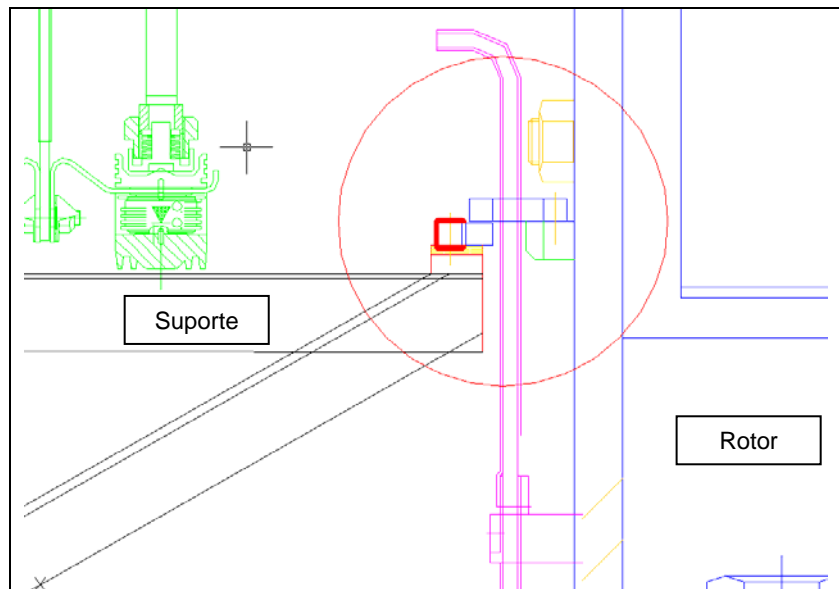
Desenho da Montagem do Sistema no Rotor
